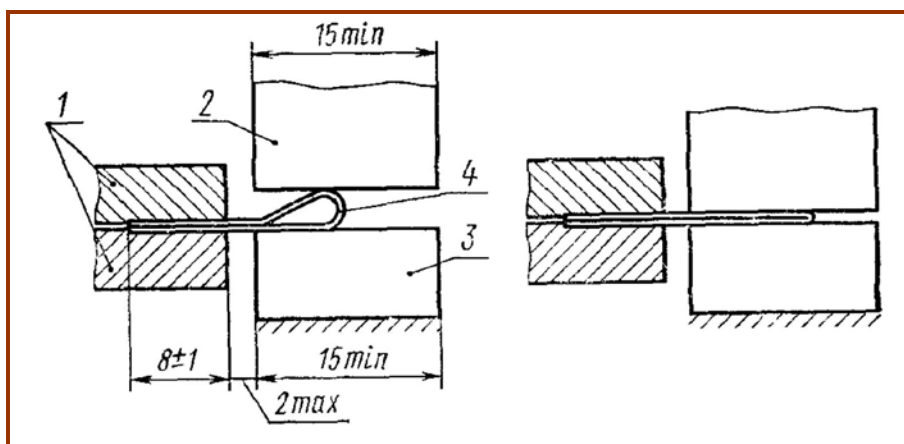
Принципова схема затискання та навантаження зразка: 1 - затискувач; 2 - пуансон для здавлювання зразка; 3 - нижня основа; 4 - випробувальний зразок
